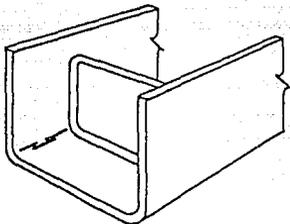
INDICACION DE POSICION Y EXTENSION DE SOLDADURA DE FILETE
